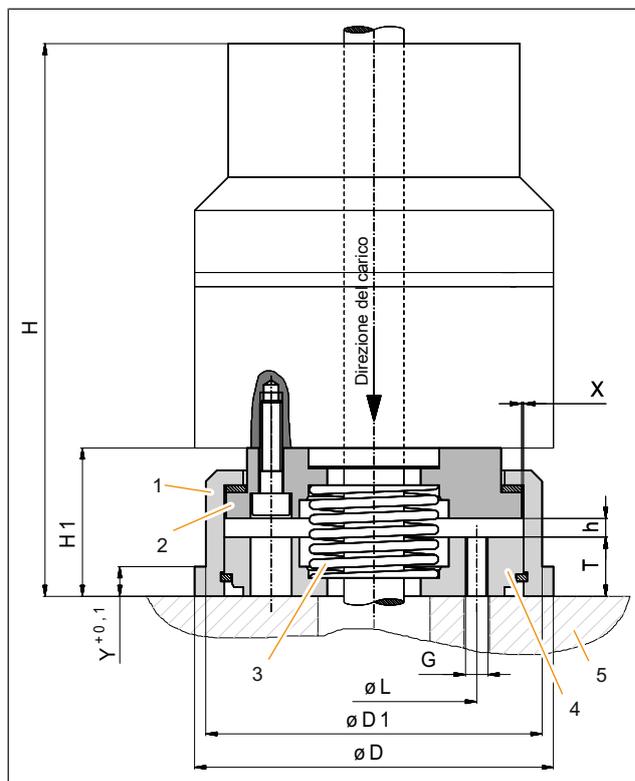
Dimensioni della base a molla per freni di sicurezza
